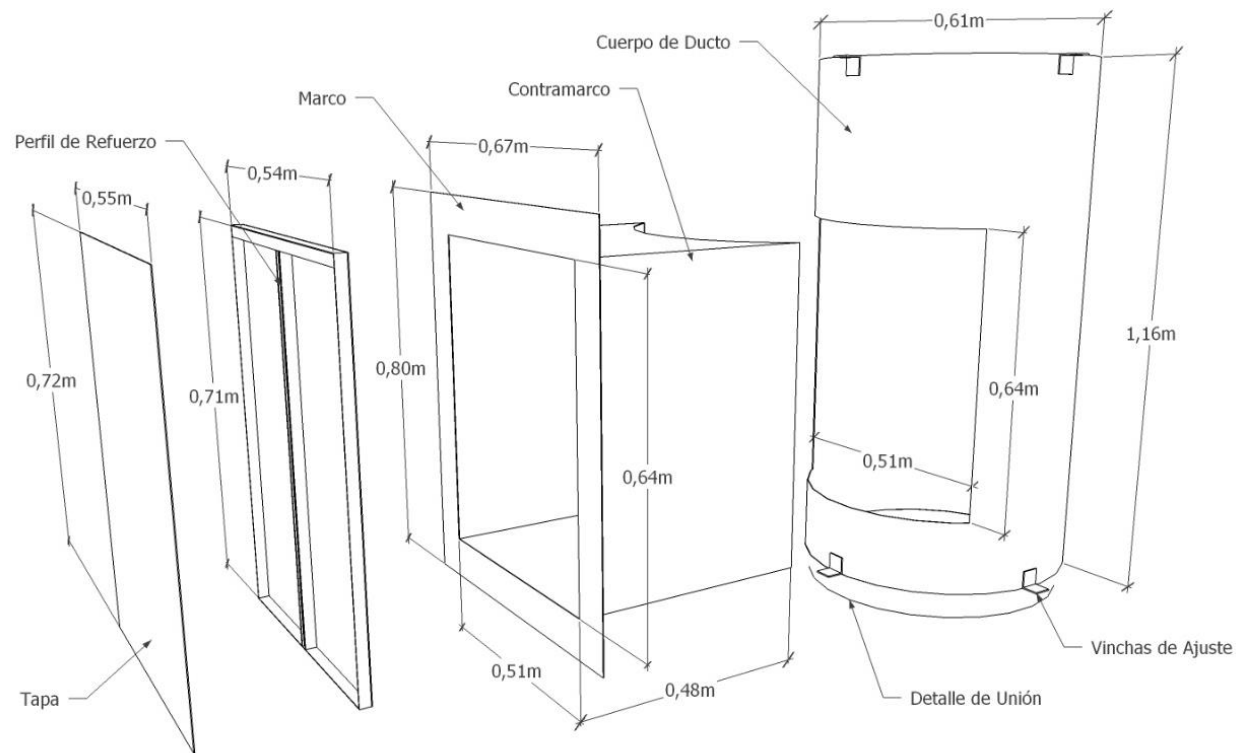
Ensamblaje de Puerta de Mantenimiento.
